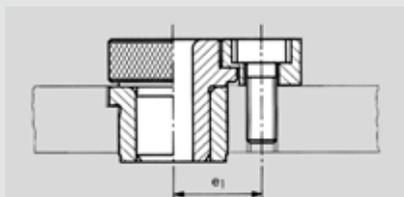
Schnellwechslbuchse Form K mit eingelassener Bundbohrbuchse DIN 172 oder zylindrischer Bohrbuchse DIN 179. Die Befestigung erfolgt mit Spannbuchse DIN 173 und Zylinderschraube DIN 912. Die Schnellwechslbuchse Form K kann auch mit Anschlagstift gesichert werden. Diese Befestigungsmöglichkeit ist nicht für langspannende Werkstoffe vorzusehen (Unfallgefahr).
